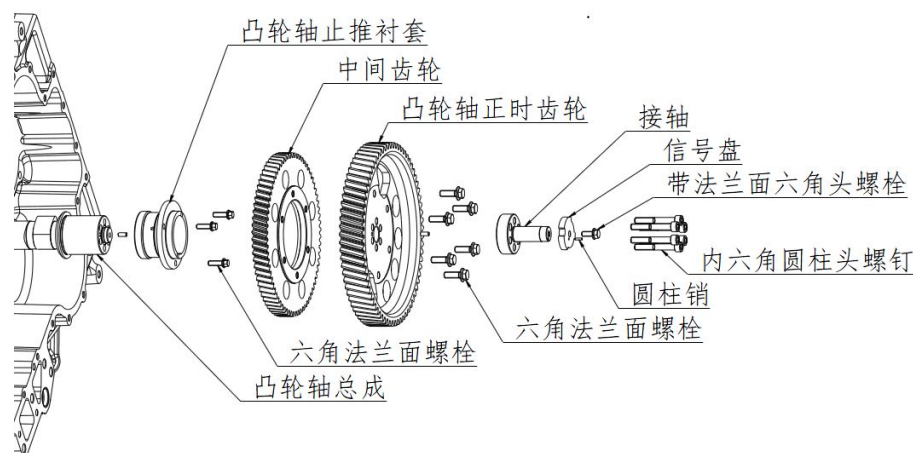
Распределительный вал и ГРМ дизельного двигателя карьерного самосвала 16M33.
